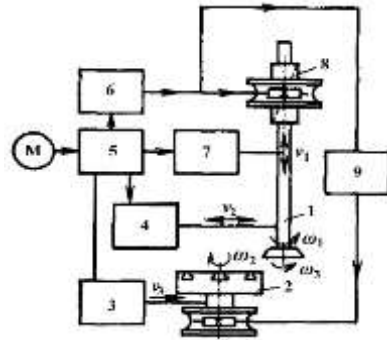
Принципова схема зубодовбального верстата з механічними кінематичними зв'язками
